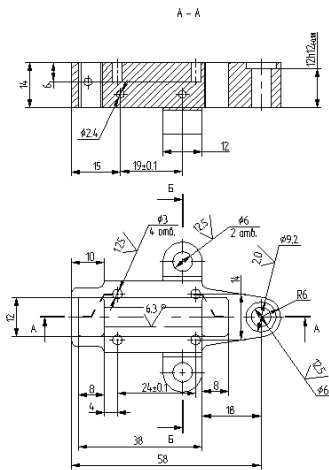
Фрагмент чертежа детали с Н-образным пазом
